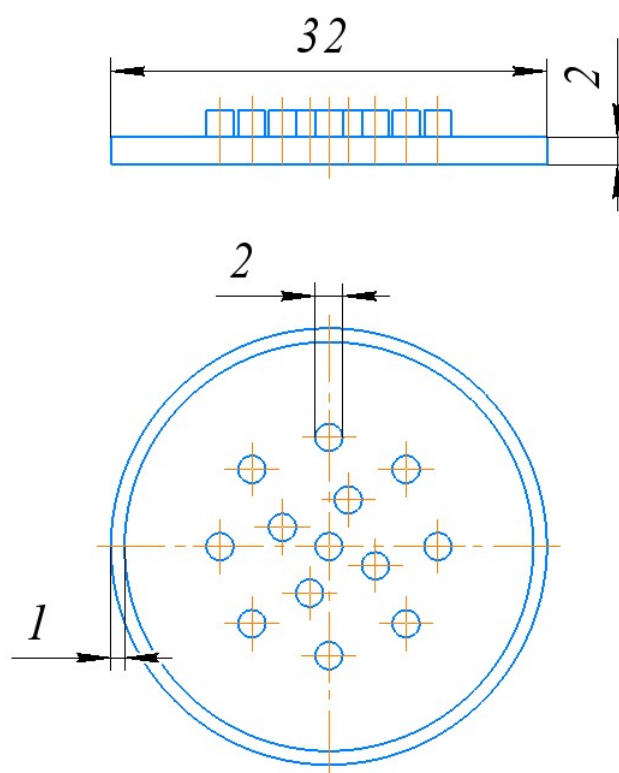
Креслення пропонованої конструкції кришки
